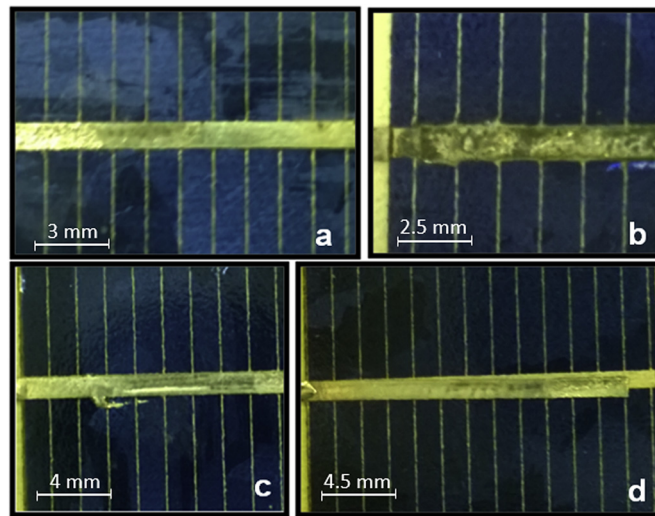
Tipos de configuraciones de soldadura observadas visualmente en las celdas: (a) buena cinta soldada; (b) exceso de material de soldadura en las proximidades de la cinta; (c) exceso de material de soldadura goteó sobre el dedo y (d) cinta dislocada en la parte superior de la barra colectora.
